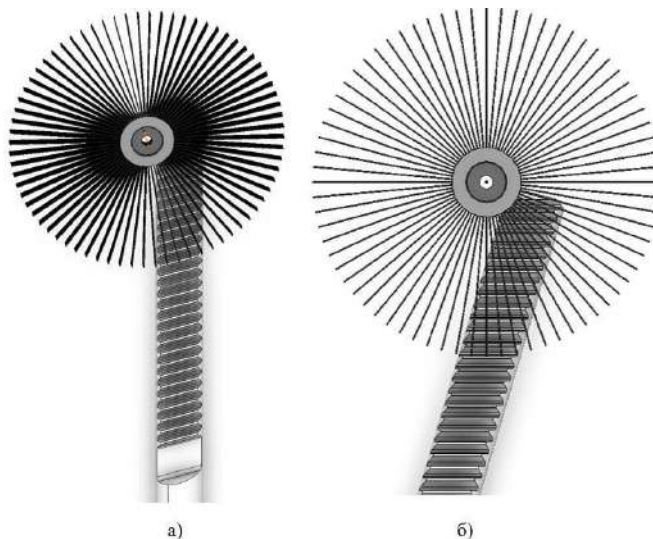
Обробка рульової рейки гнучким інструментом: а – вид зверху; б – вид нормаллю до інструменту
